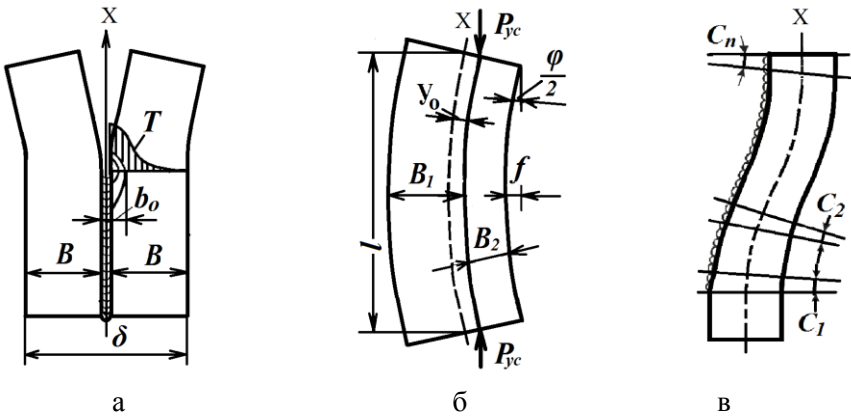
Деформації зварного виробу при однаковій ширині зварюваних пластин (а), при різній ширині зварюваних пластин (б) та при наплавленні валика на край пластини.
